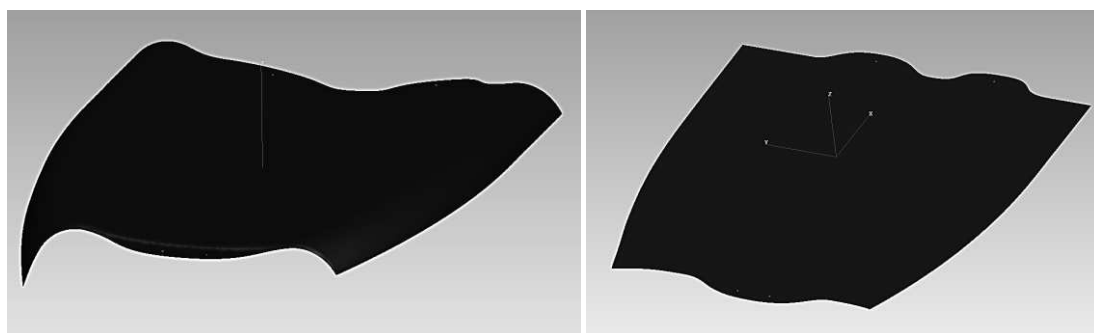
Формирование развертки детали: а – исходная деталь; б – точная развертка
